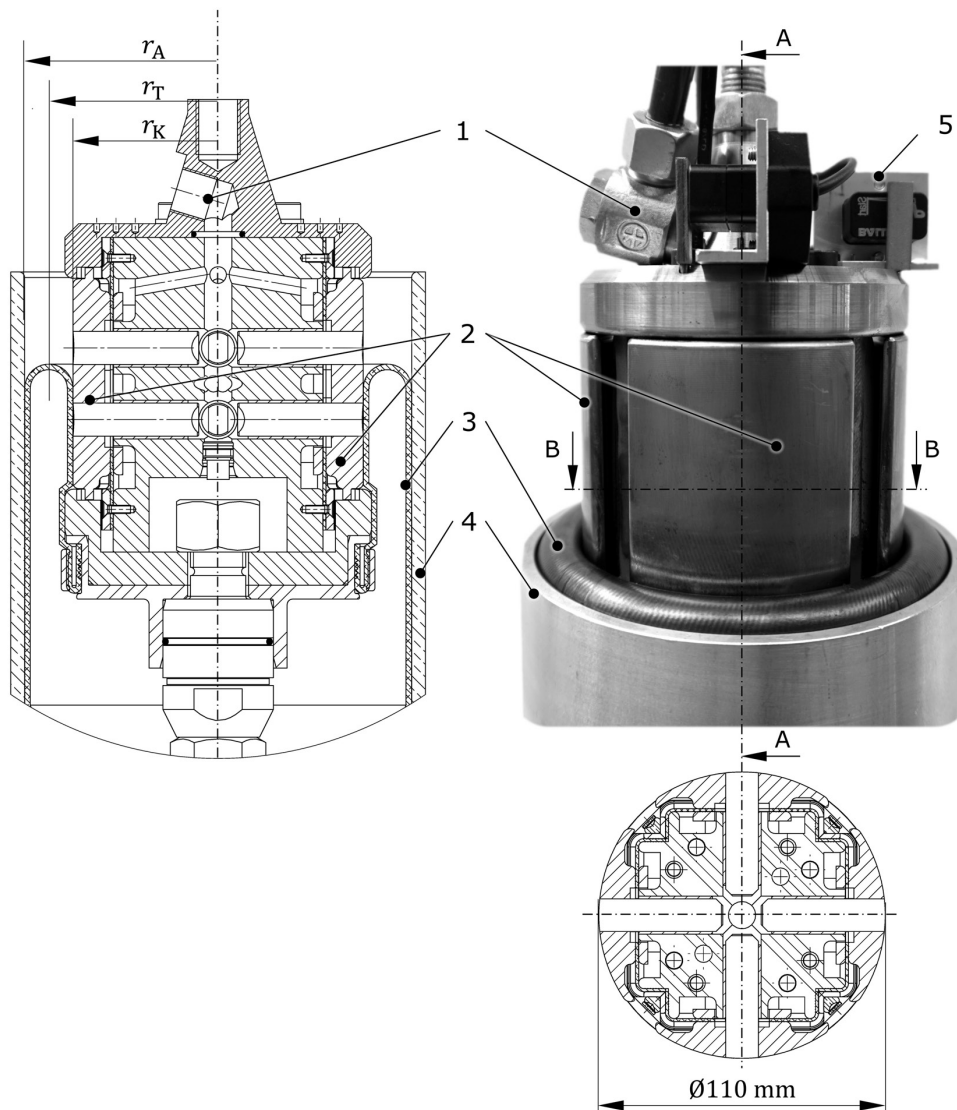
Der Luftfederabrollkolben mit hydraulisch verstellbarem Kolbendradius r_K . (1) ist der hydraulische Anschluss, (2) die verfahrbaren Segmente, (3) der Luftfederrollbalg und (4) die Luftfederaußenführung. Im Versuch wird die Position der Abrollkolbensegmente mit induktiven Sensoren (5) gemessen.
